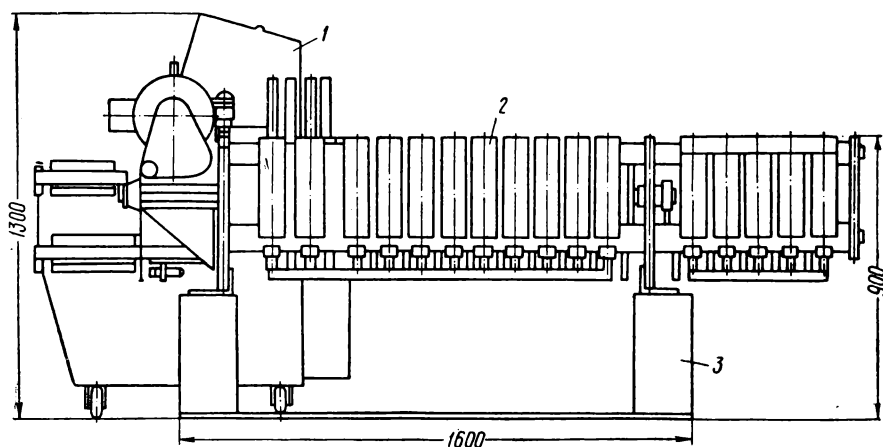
Стенд для ремонта и испытания главного контроллера ЭКГ-8:
